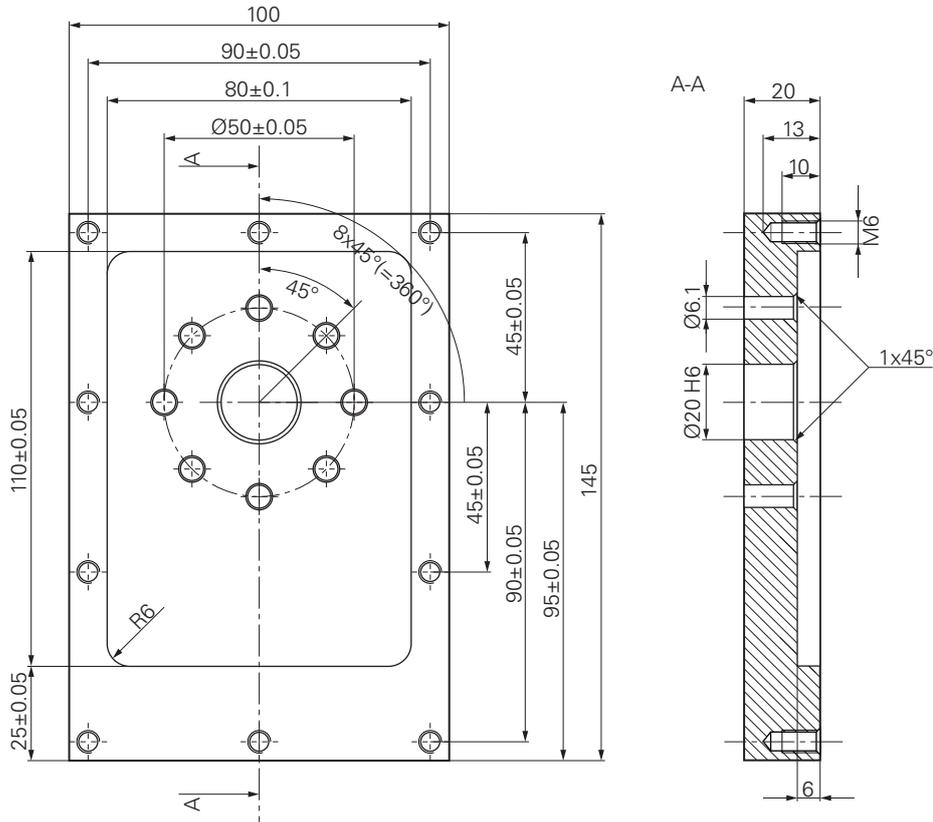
Beispielwerkstück – Technische Zeichnung
